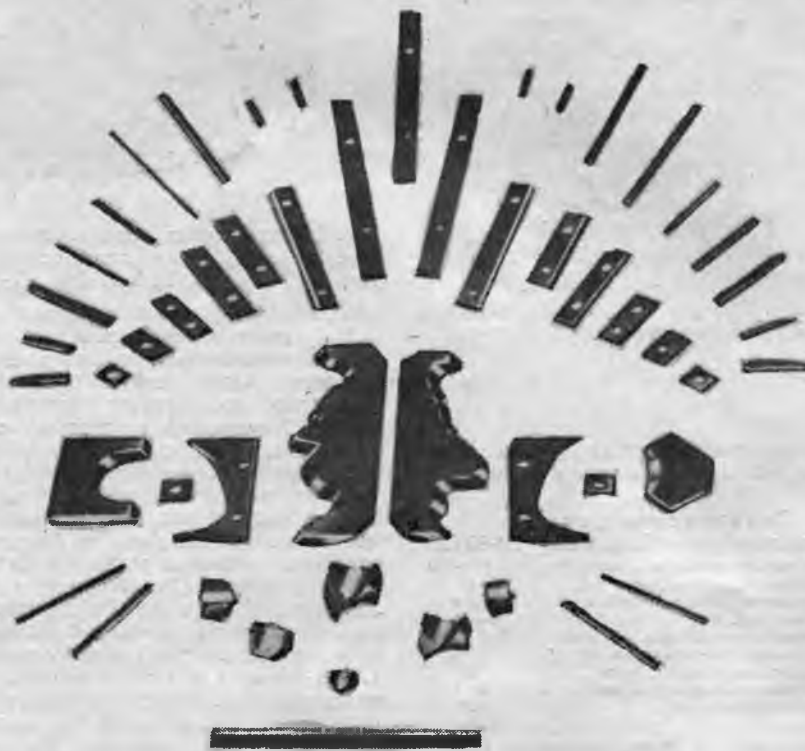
Твердосплавные пластинки для дереворежущего инструмента
